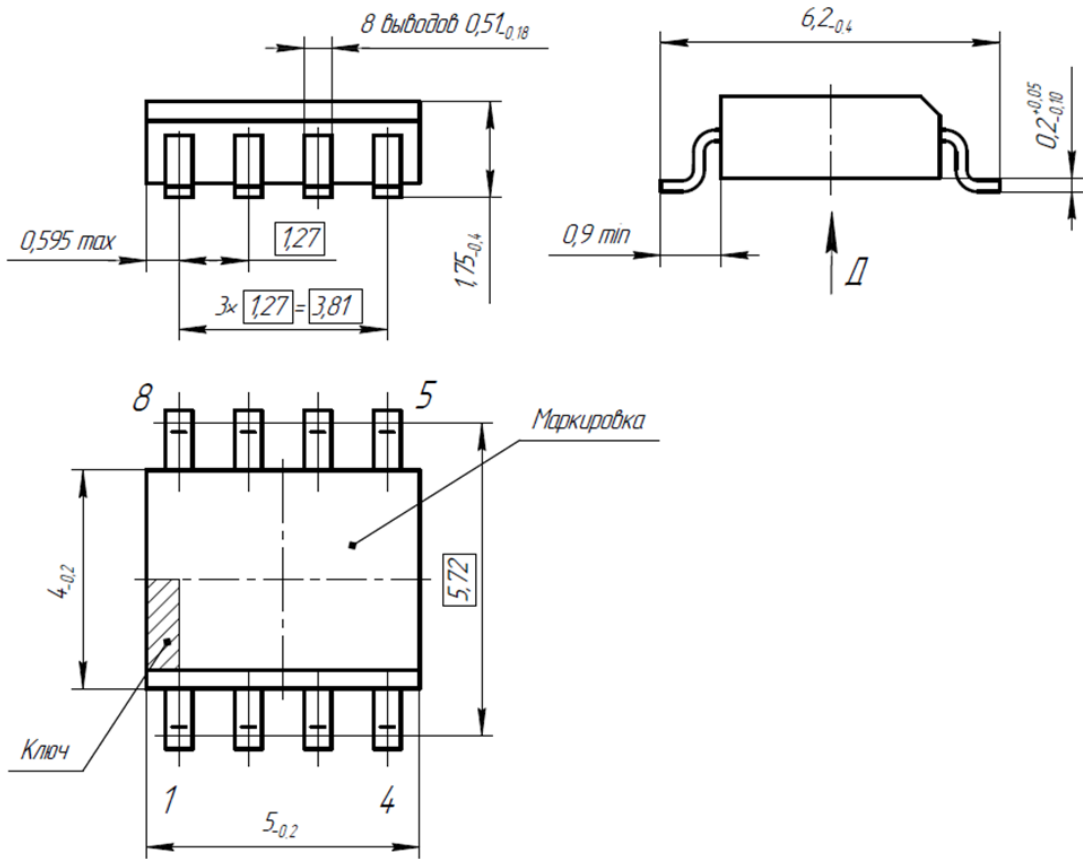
Внешний вид корпуса 4303Ю.8-А
